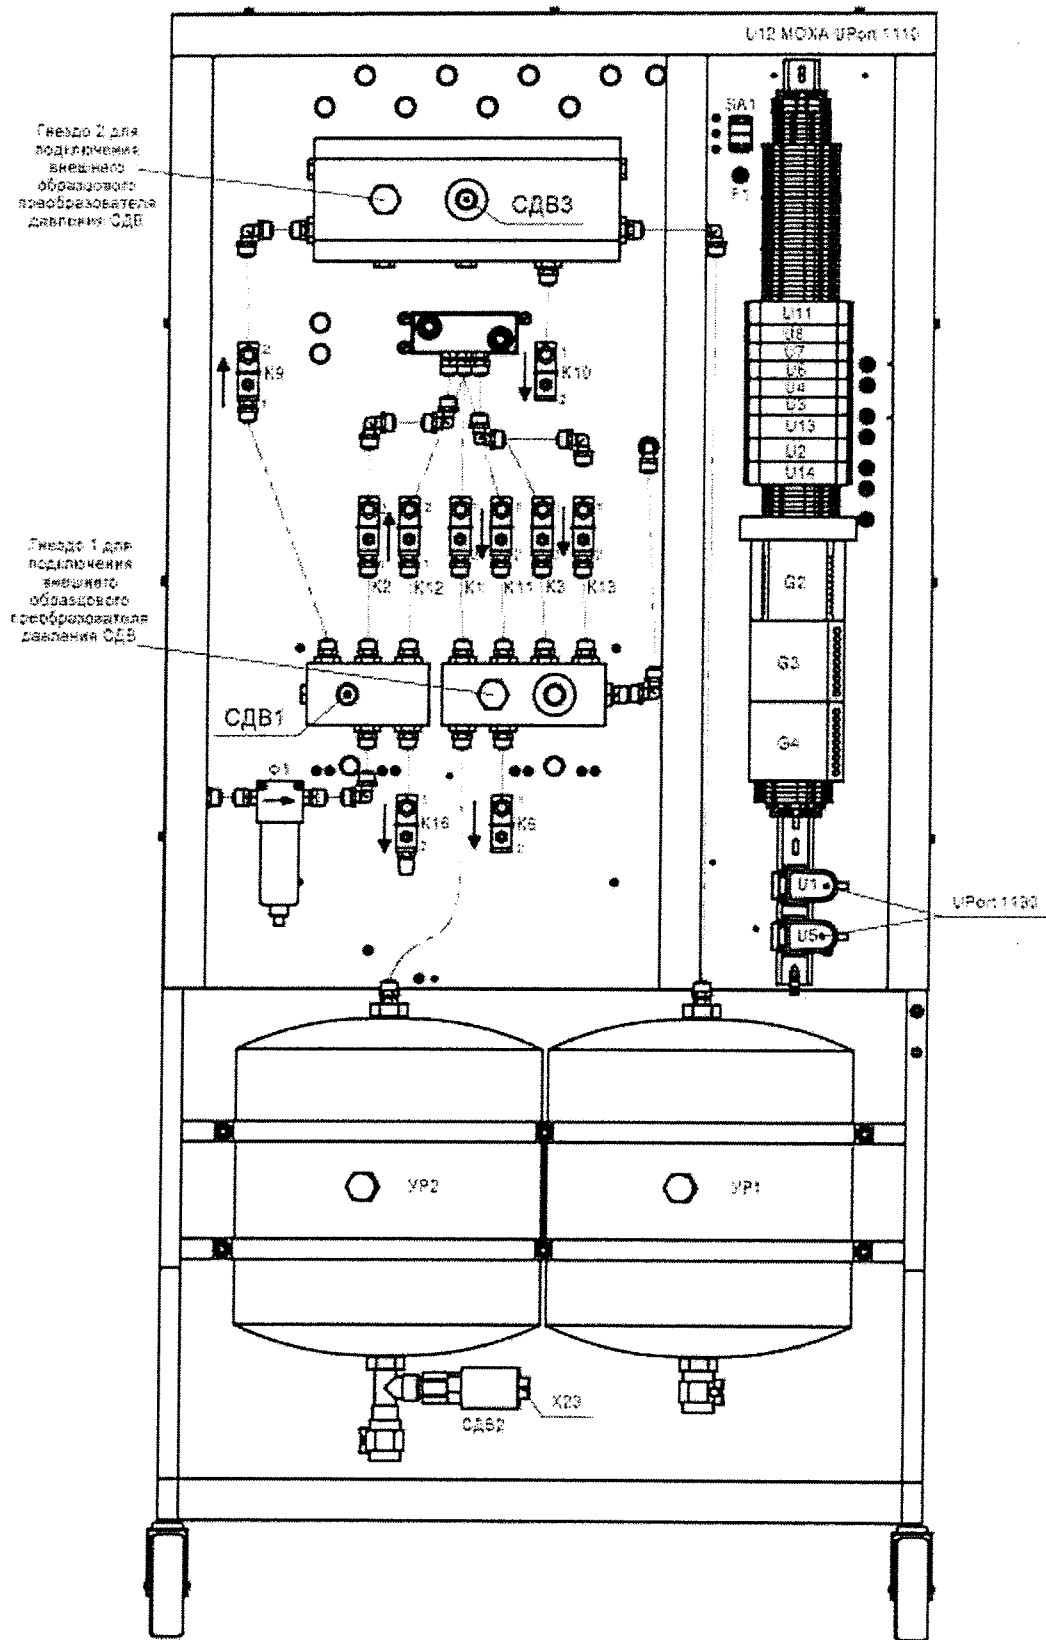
Внешний вид УПИ-ДД и размещение приборов вид сзади без кожуха
